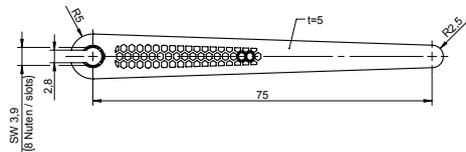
Werkzeug für Kabelmontage Typ 1300A185C
